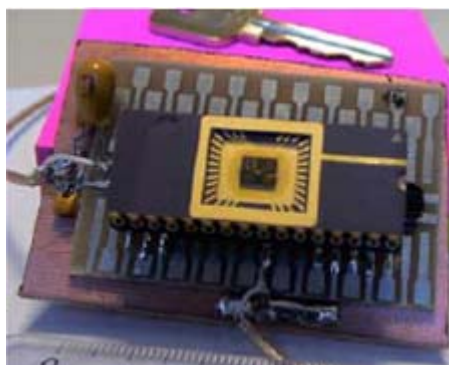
In primo piano è mostrato il package, il chip con gli SPAD e la basetta su cui sono saldati i componenti discreti del circuito di quenching passivo.
